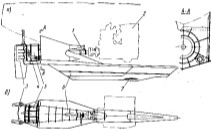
Схема водометного движителя теплохода «Чапаев»: а — вид сверху; б — вид спереди.
